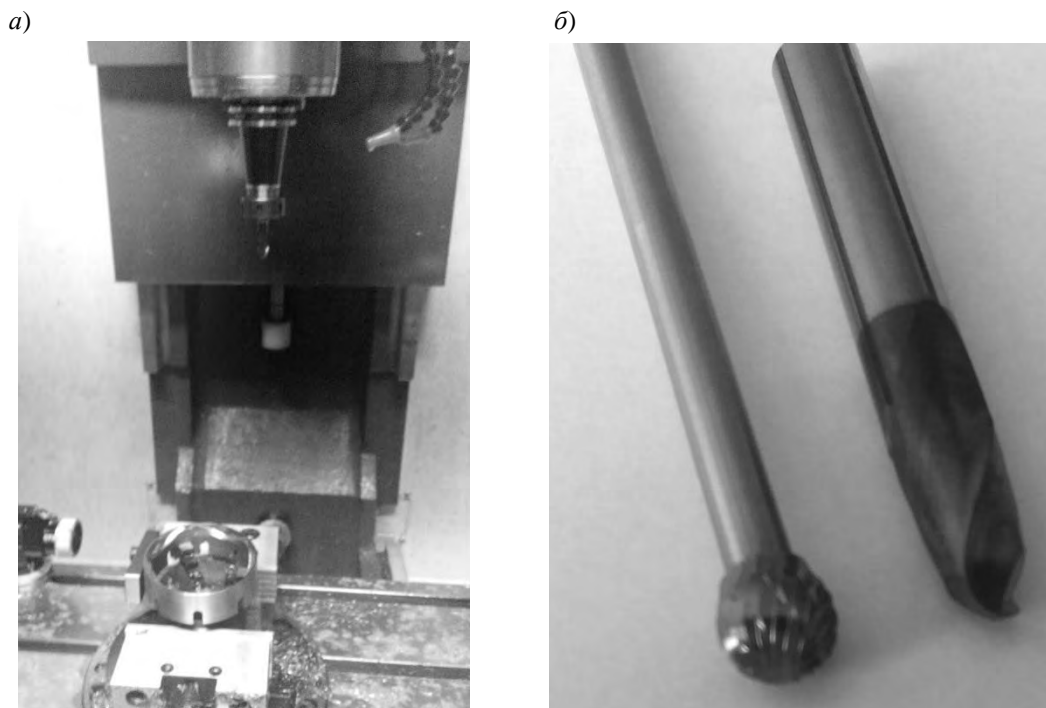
Изготовление сферических кулачков: а – обработка дорожки на вертикально-фрезерном станке с ЧПУ; б – применяемые виды сферических фрез (слева – шаровидная бор-фреза; справа – двузубая концевая фреза со сферическим торцом)
